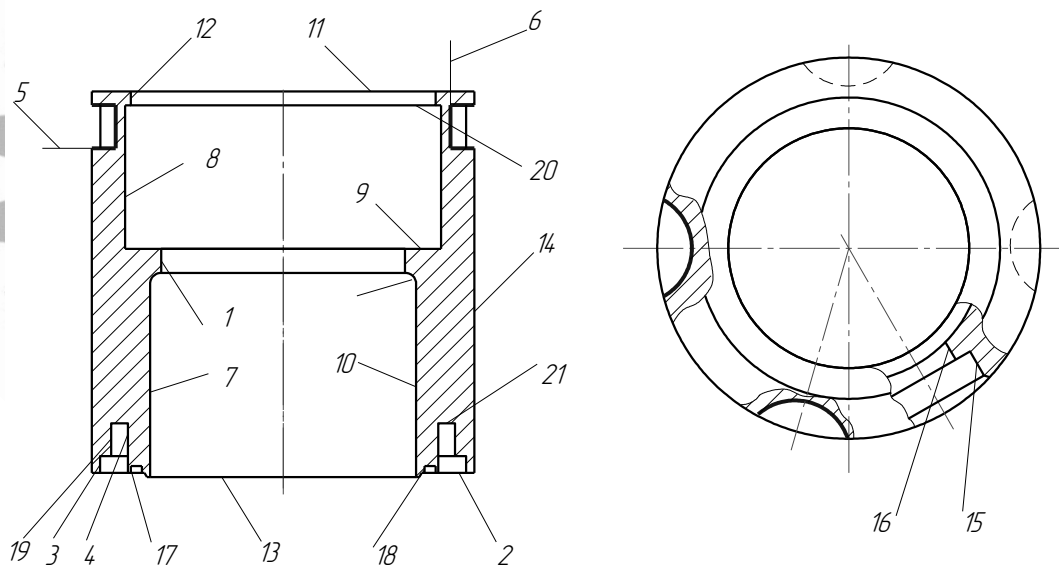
Эскіз деталі «Корпус ЦФ7.180.187»
